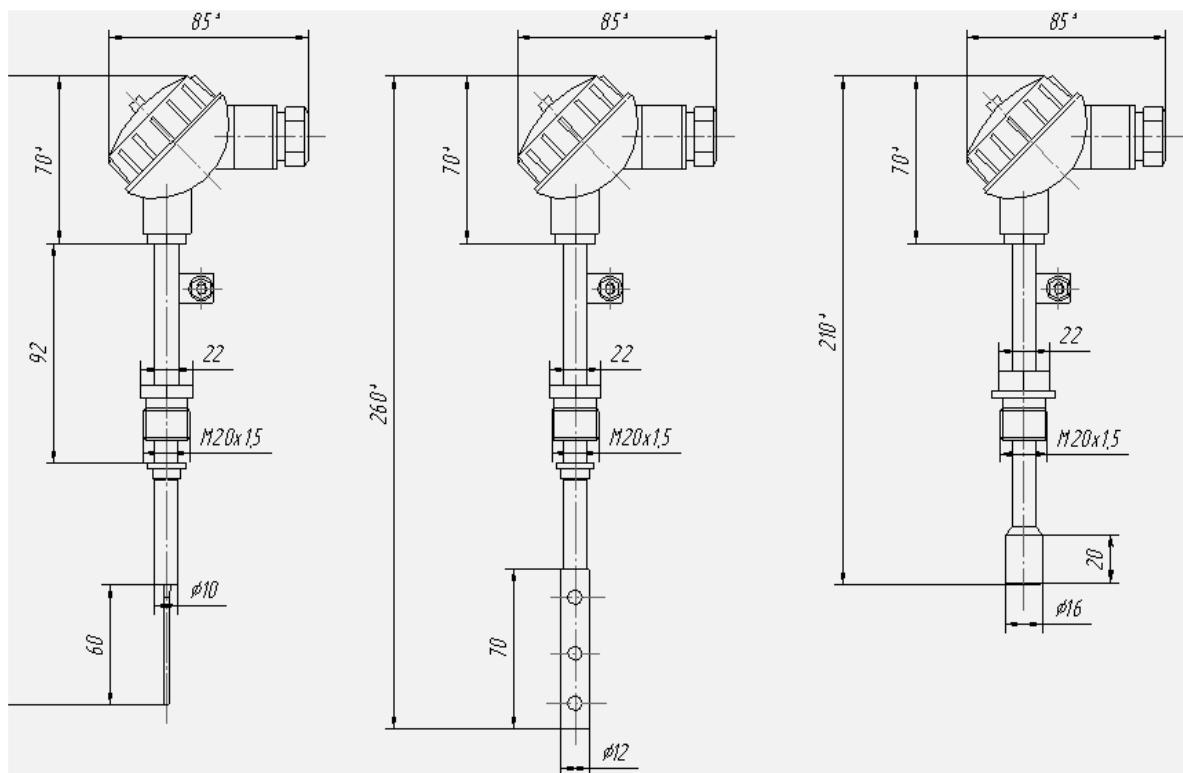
Внешний вид и габаритные размеры сигнализатора СЖУ-1-Э:
